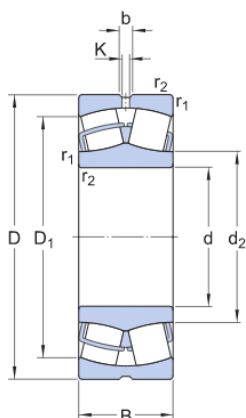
Diagrama con dimensiones de rodamientos de rodillos. Fuente: www.skf.com.
